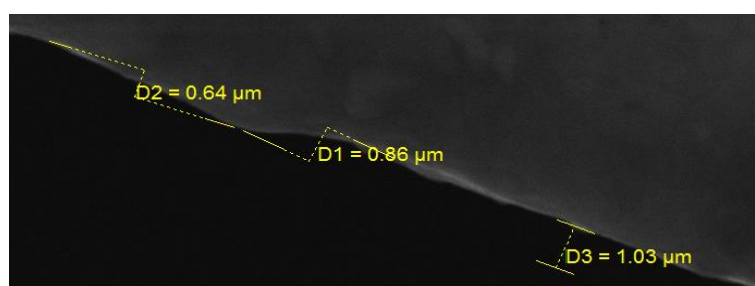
Mínimo desgaste de la Herramienta de corte para el ensayo 13.
